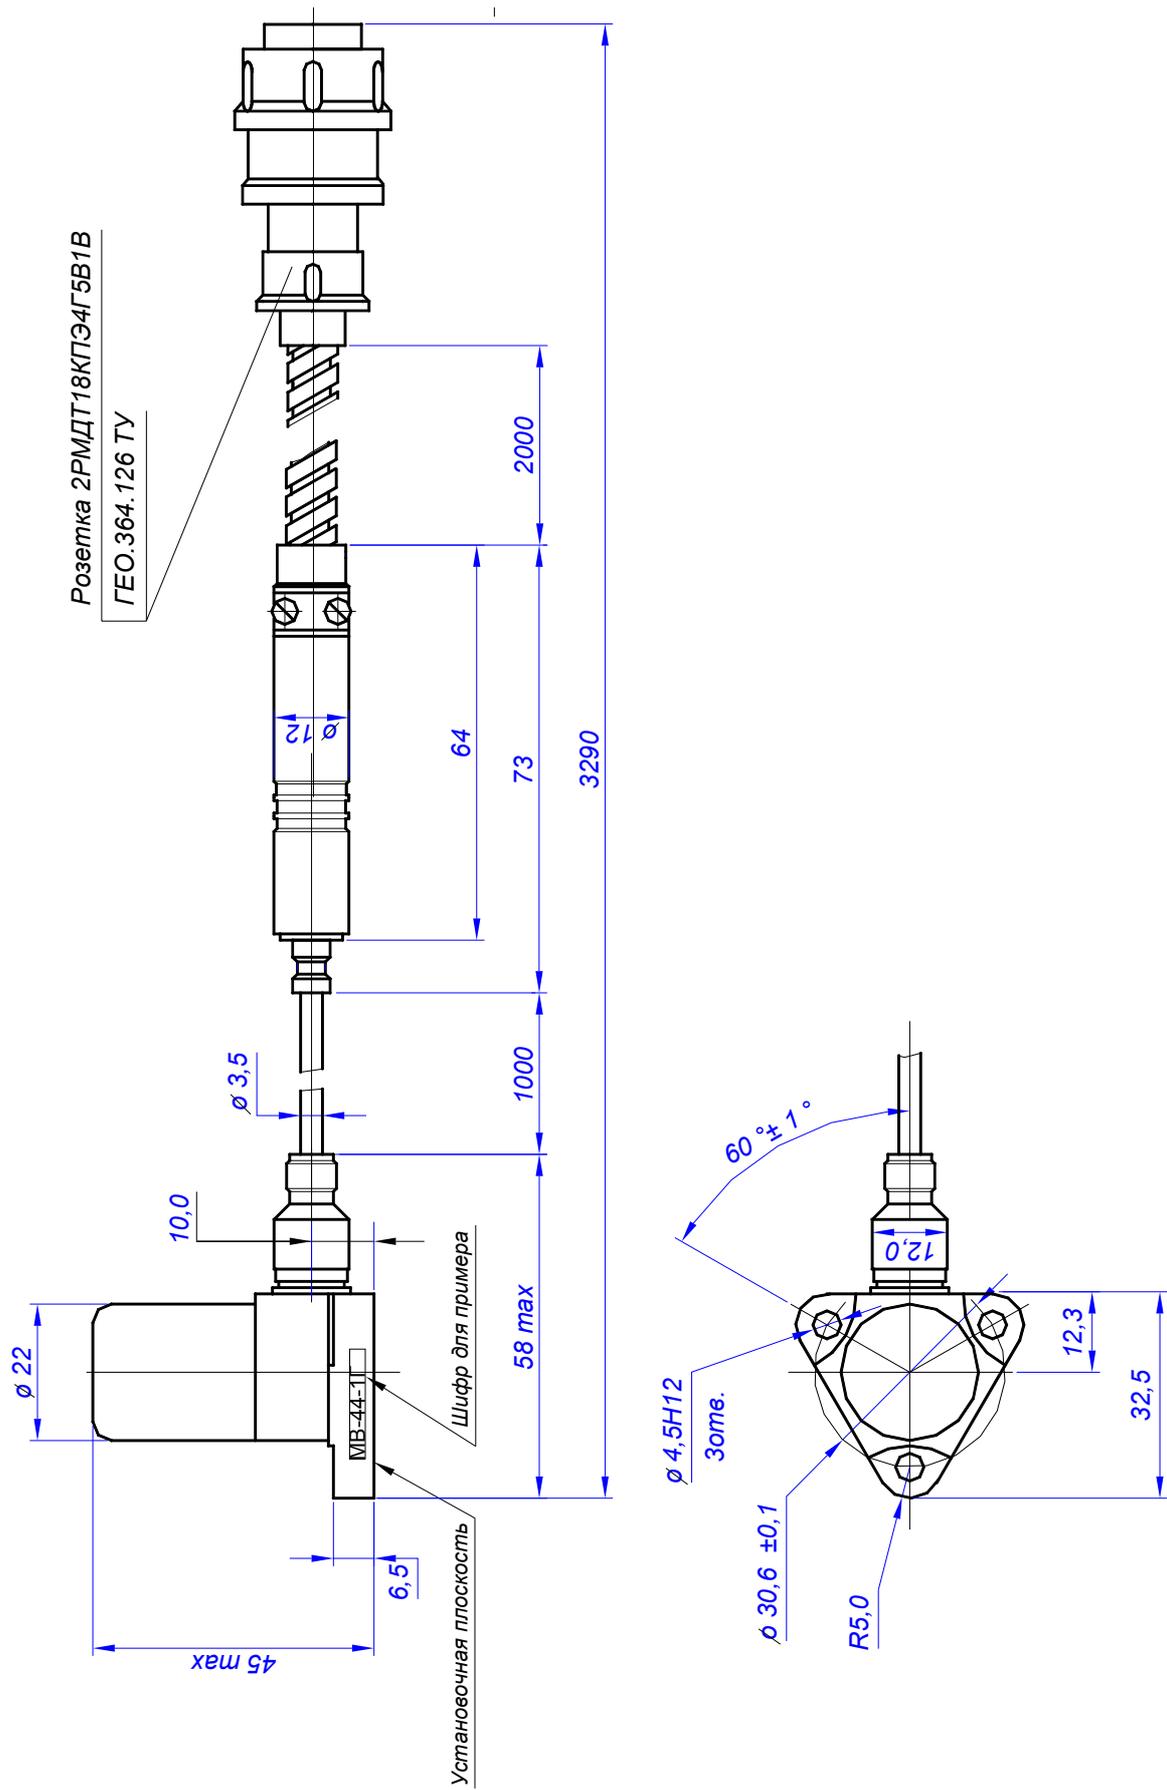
Габаритно-установочные размеры вибропреобразователя MB-44-1Г/1,0/2,0
